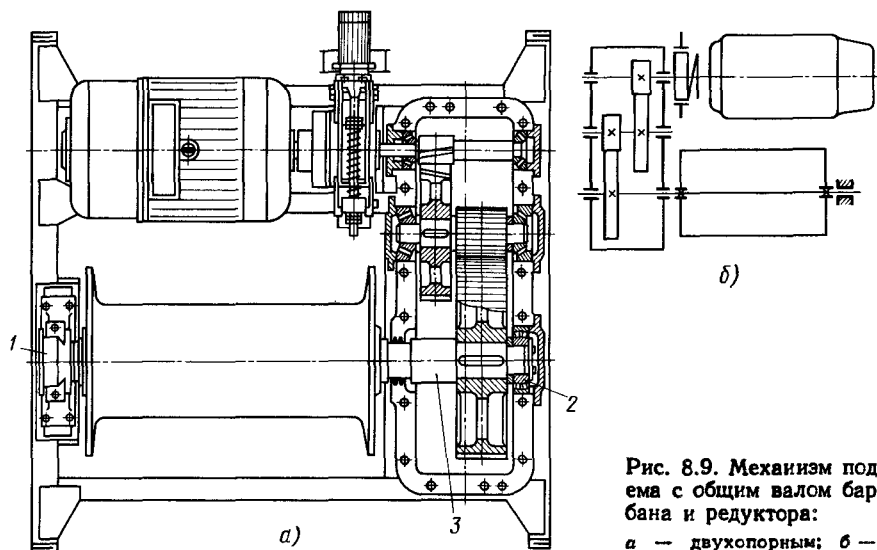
Механизм подъема с общим валом барабана и редуктора:
